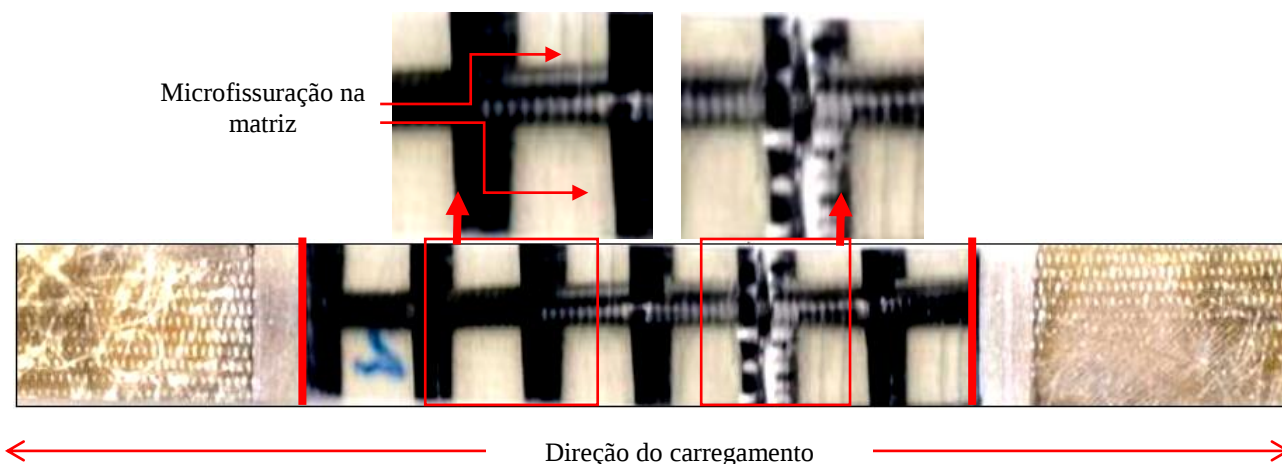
Característica da fratura final – Laminado LVC – Estado original
